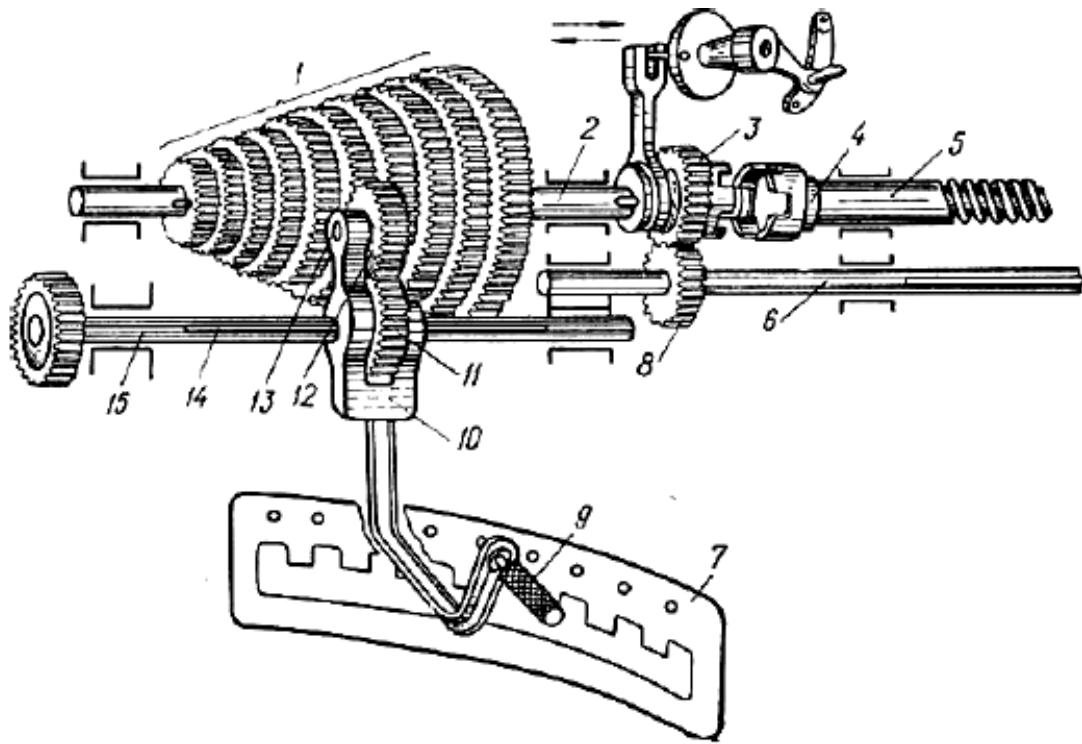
Коробка подач: 1 – блок; 2, 15 – вал; 3, 8, 11, 12 – зубчасті колеса; 4 – муфта; 5 – ходовий гвинт; 6 – ходовий валик; 7 – шкала; 9 – рукоятка; 10 – обойма; 13 – ось; 14 – фіксатор зубчастого колеса на валу
